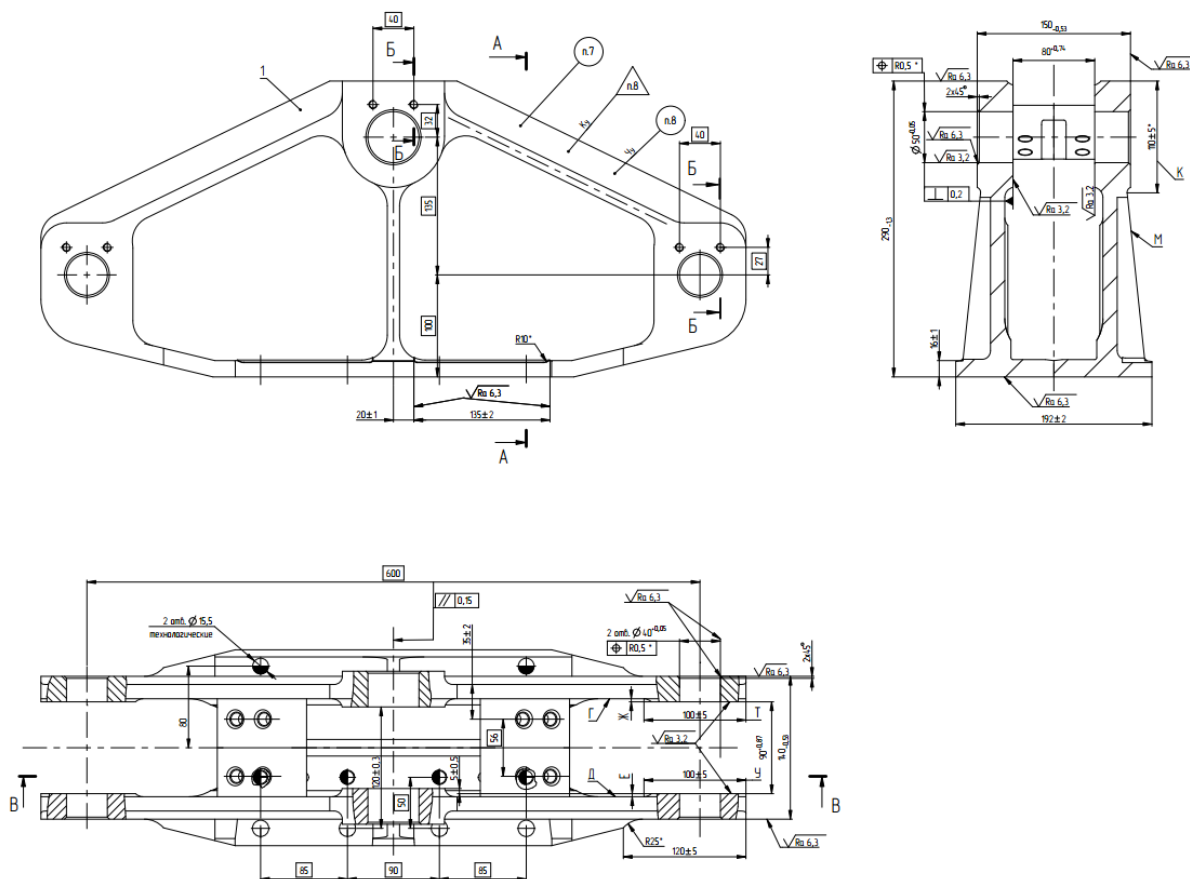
Чертеж сборочной единицы «Корпус»
